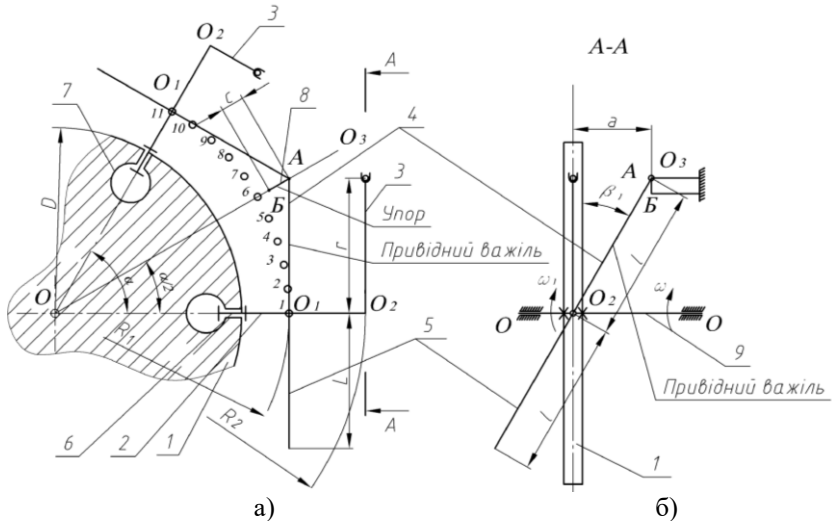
Розрахункова схема черпакового механізму сівалки точного висіву: 1-диск; 2-вісь важільного механізму; 3-черпак з плечем; 4-привідний важіль; 5-важіль повертання важільного механізму у вихідне положення; 6-шарнір осі важільного механізму; 7-технологічний отвір; 8-упор; 9-привідний вал
